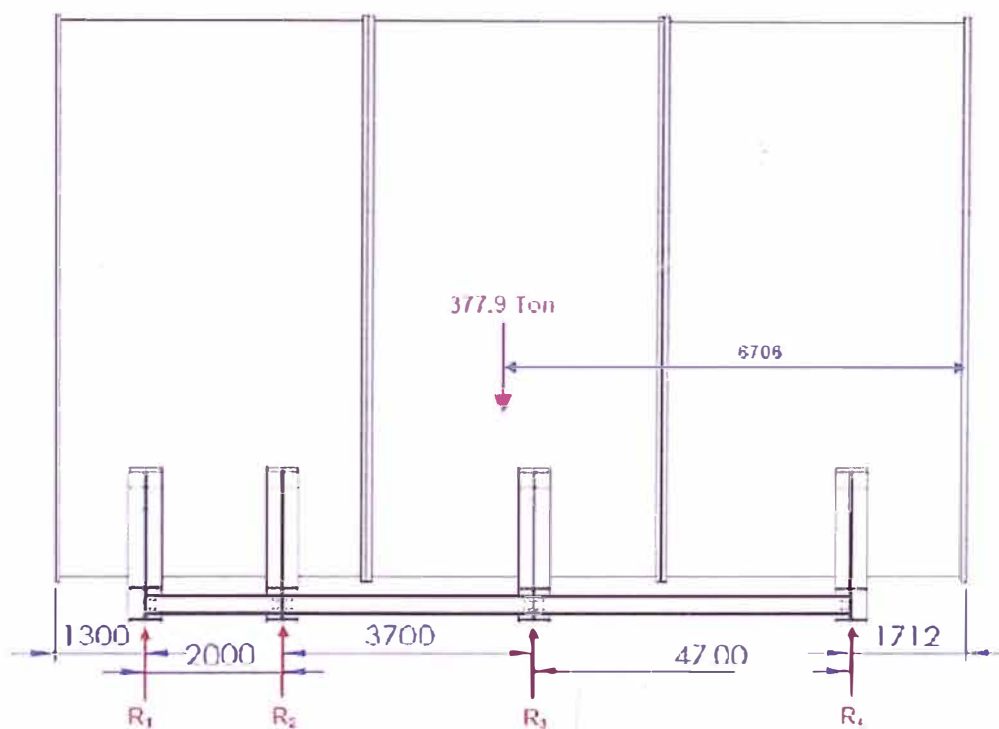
Distribución de 4 cunas, para montaje de las 3 virolas o secciones del Shell del molino de bolas en piso.
